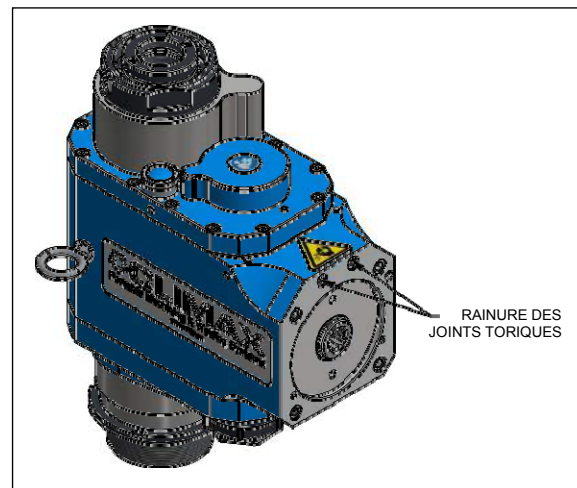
EMBLACEMENT DU JOINT TORIQUE
